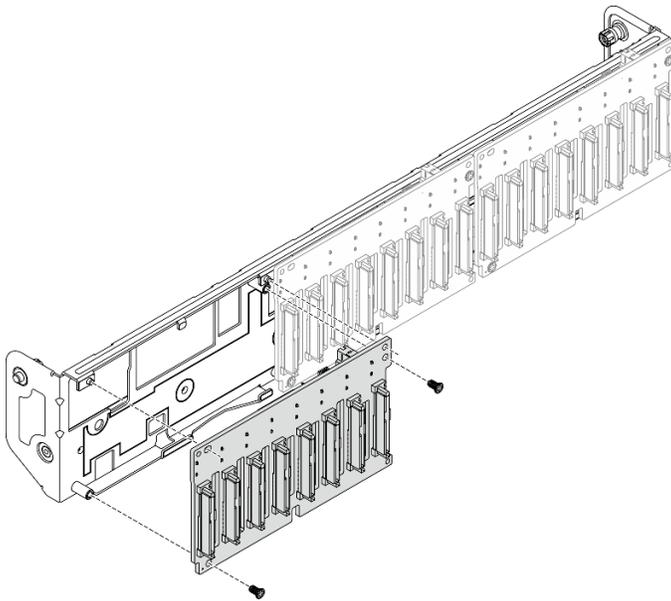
Installation du fond de panier sur le support (châssis doté d'une baie E3.S)
